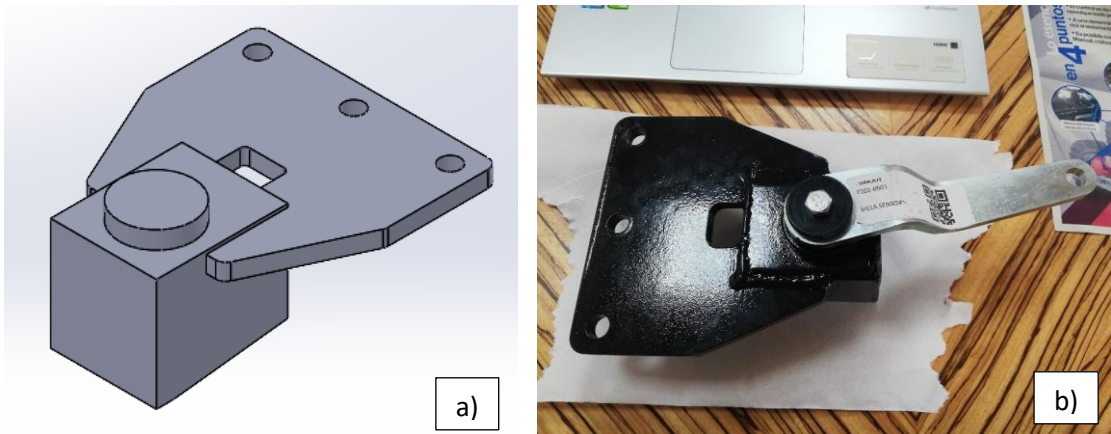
Desenho 3D (a) e imagem real do sensor angular dianteiro (b)
